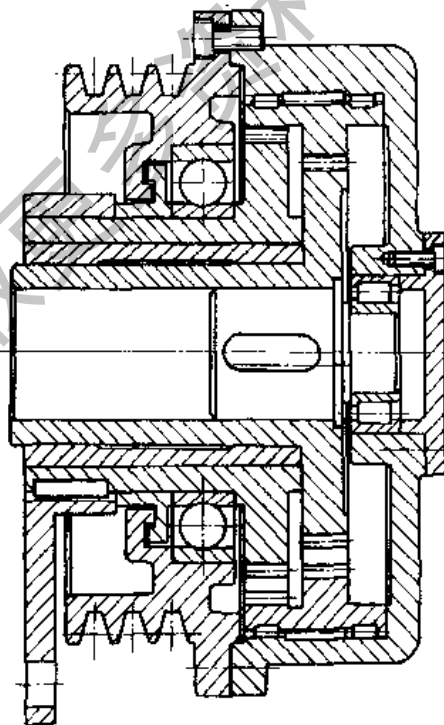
轴向尺寸小的 2Z-X 型少齿差减速器
